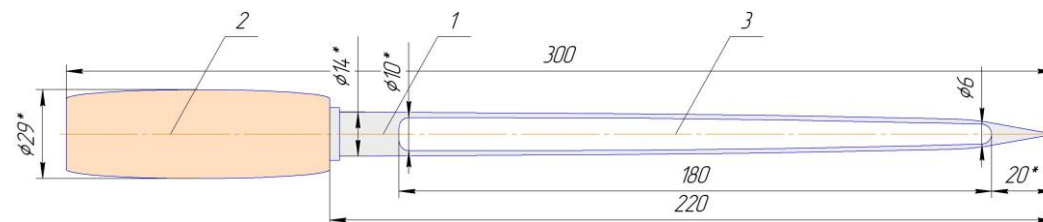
Щуп мешочный ЩМ-2: 1 – пробоотборная трубка; 2 – ручка; 3 – паз.
